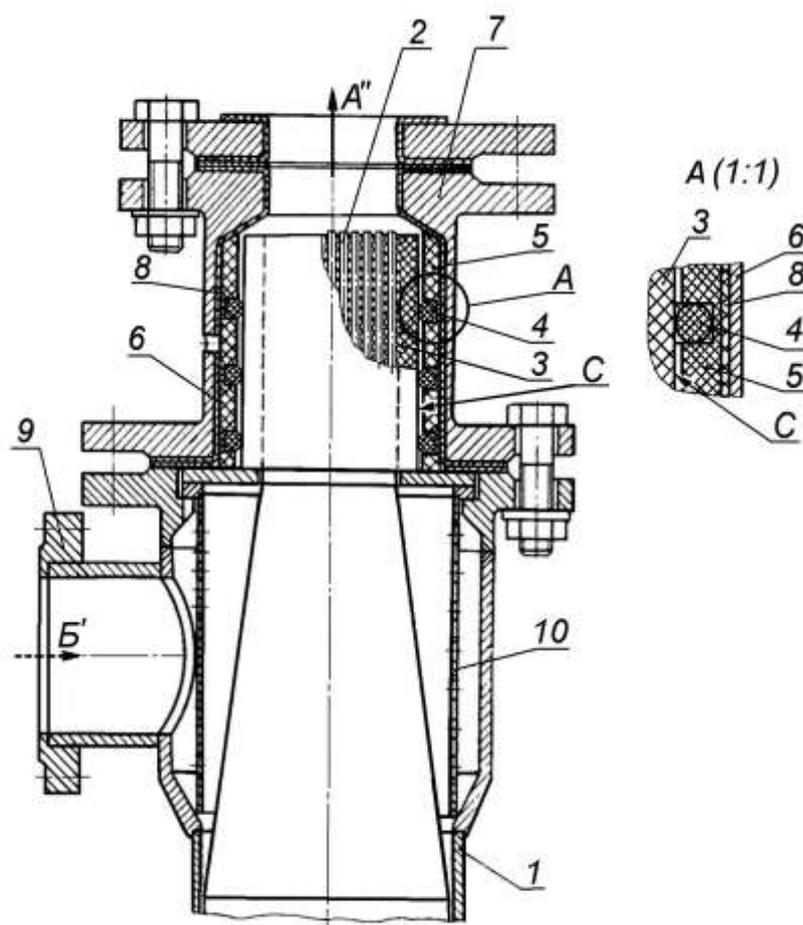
Кожухотрубчатый теплообменник с фторопластовыми трубами 2 нежесткого типа с уплотнением подвижной трубной решетки 3 плавающей головки с помощью трех резиновых колец 4, размещенных на уплотнительной втулке 5. Потoki: A'' – выход агрессивной рабочей среды из трубного пространства; B' – вход неагрессивного теплоносителя в межтрубное пространство
